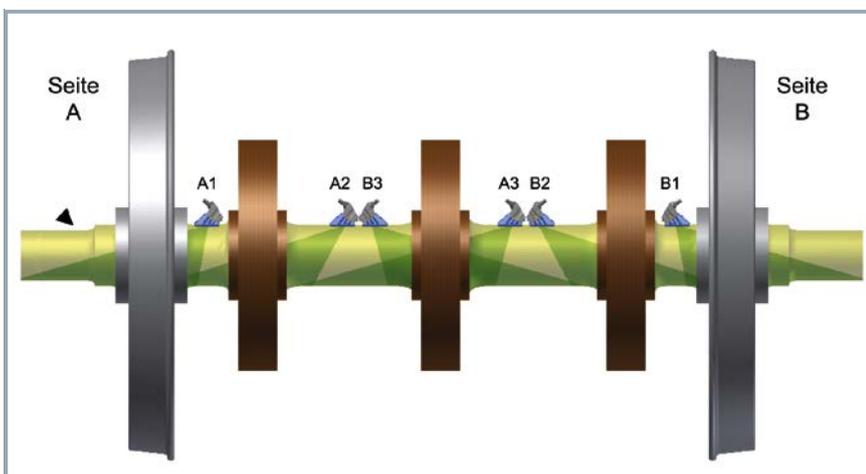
Ultraschallprüfung: Sechs Gruppenstrahler (A1 bis B3) erfassen mit einem Einschallwinkel von 33 bis 73 Grad die gesamte Wellenoberfläche. (© Fraunhofer IKTS)
